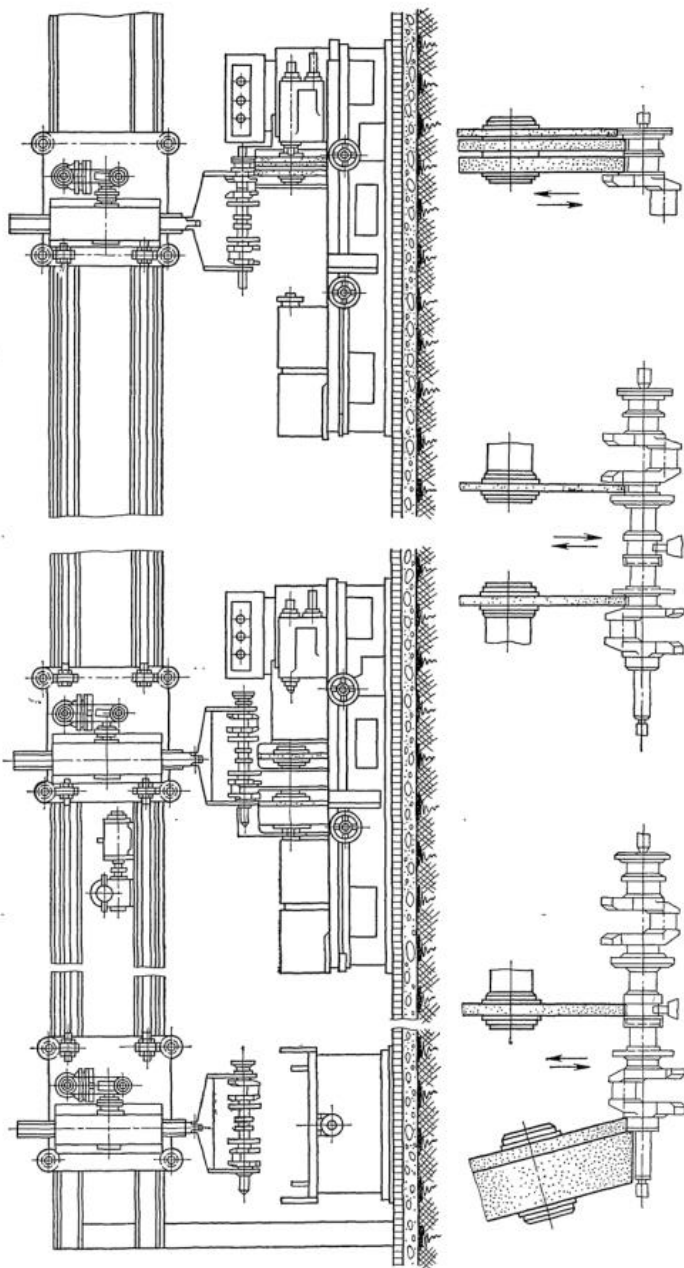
Часть автоматической линии с круглошлифовальными станками для шлифования коренных шеек коленчатого вала. Внизу показаны эскизы операций
